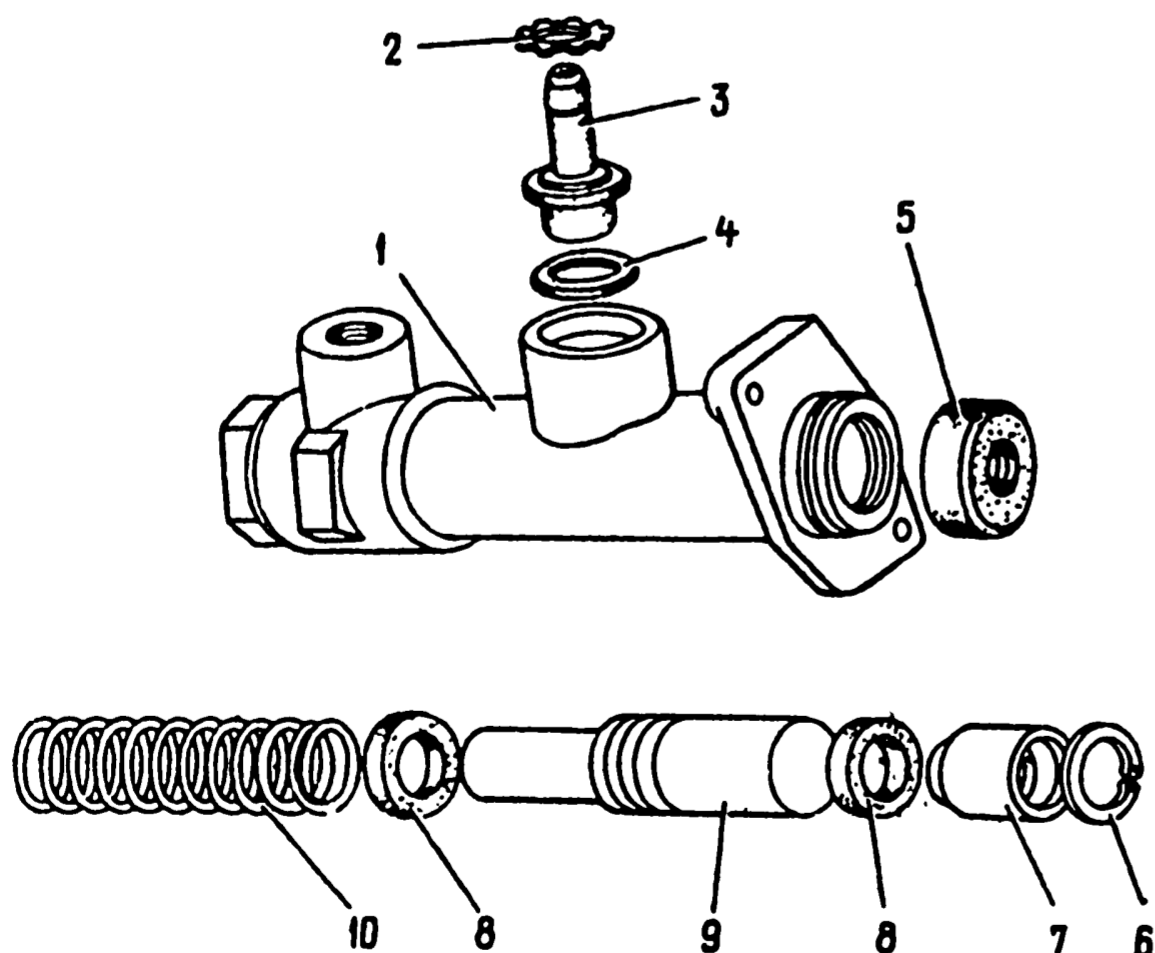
Детали главного цилиндра: 1 - корпус; 2 - стопорная шайба; 3 - штуцер; 4 - прокладка; 5 - колпачок; 6 - стопорное кольцо; 7 - поршень толкателя; 8 - уплотнительное кольцо; 9 - поршень главного цилиндра; 10 - пружина
